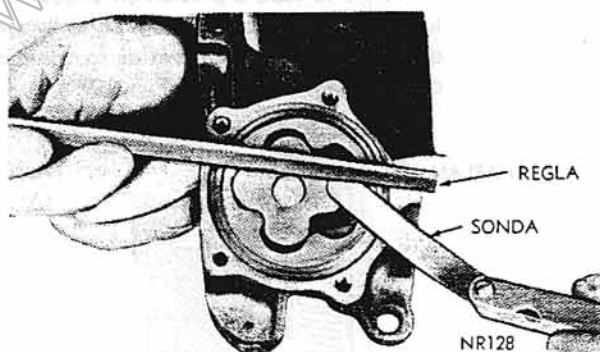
Medición de la Tolerancia sobre los Rotores
